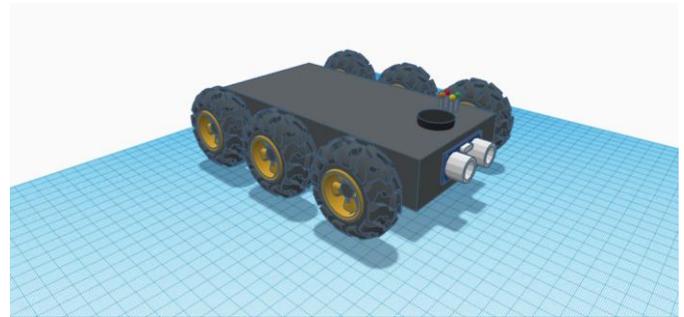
Diseño 3D del chasis y sistema de navegación. Fuente: Autores.
